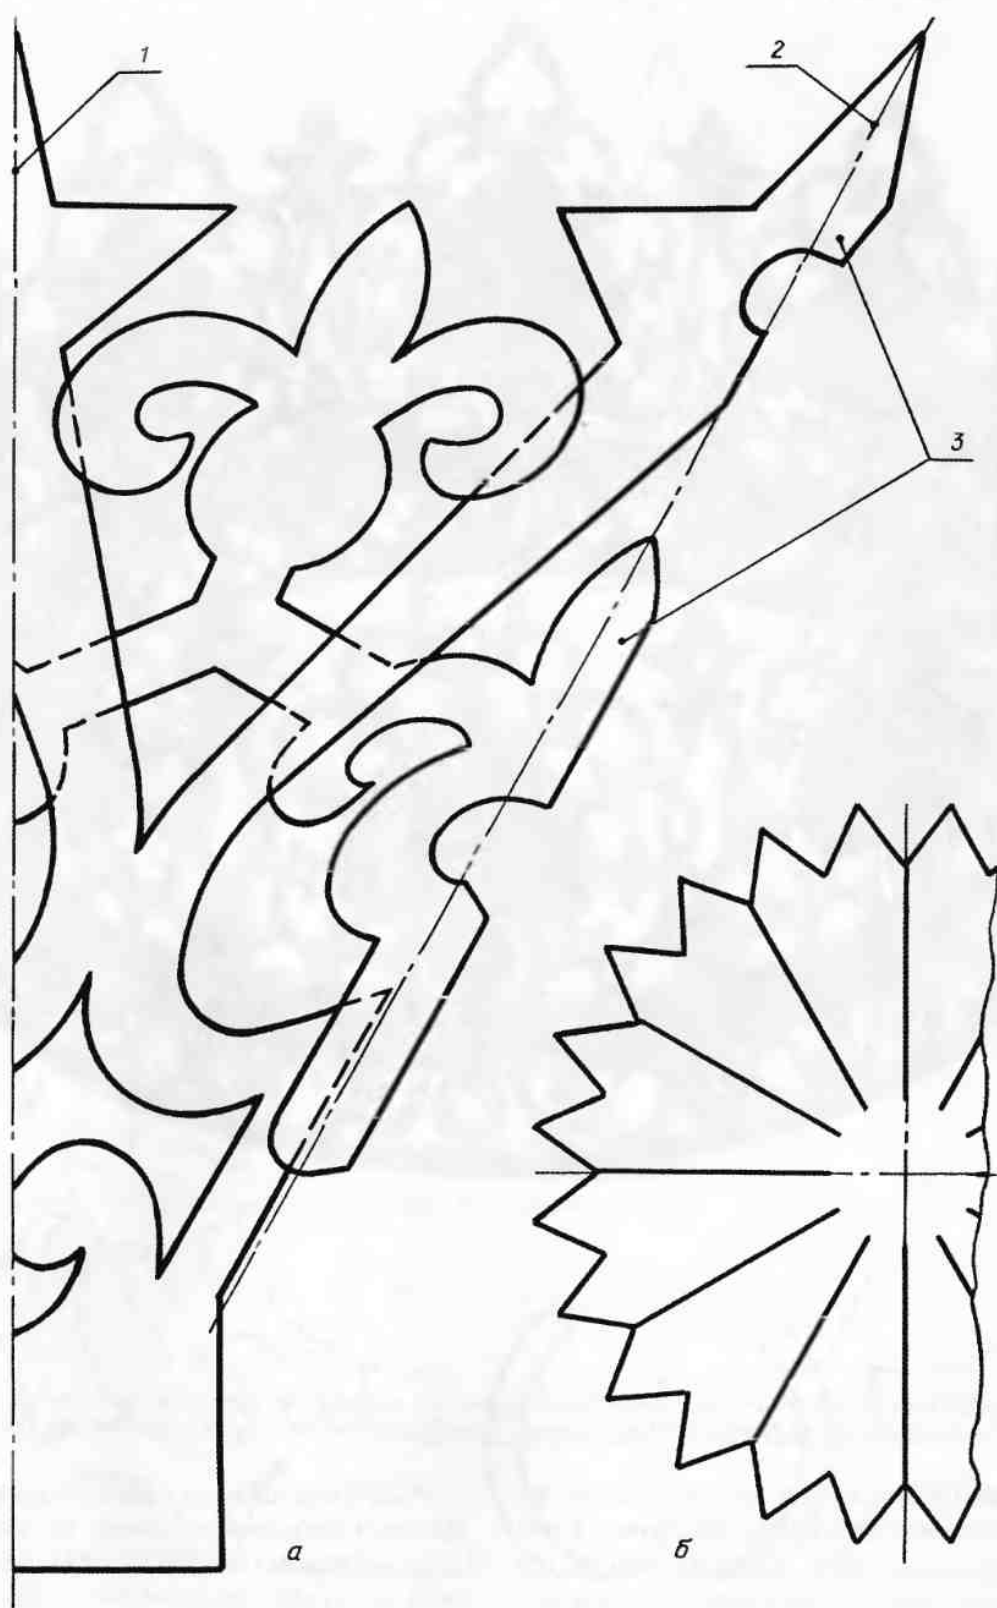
Выкройка боковой части трубы (а) и бубенца (б): 1 — линия стыка со средней частью растрёва; 2 — линия угла; 3 — кромка загиба основной и дополнительных деталей
